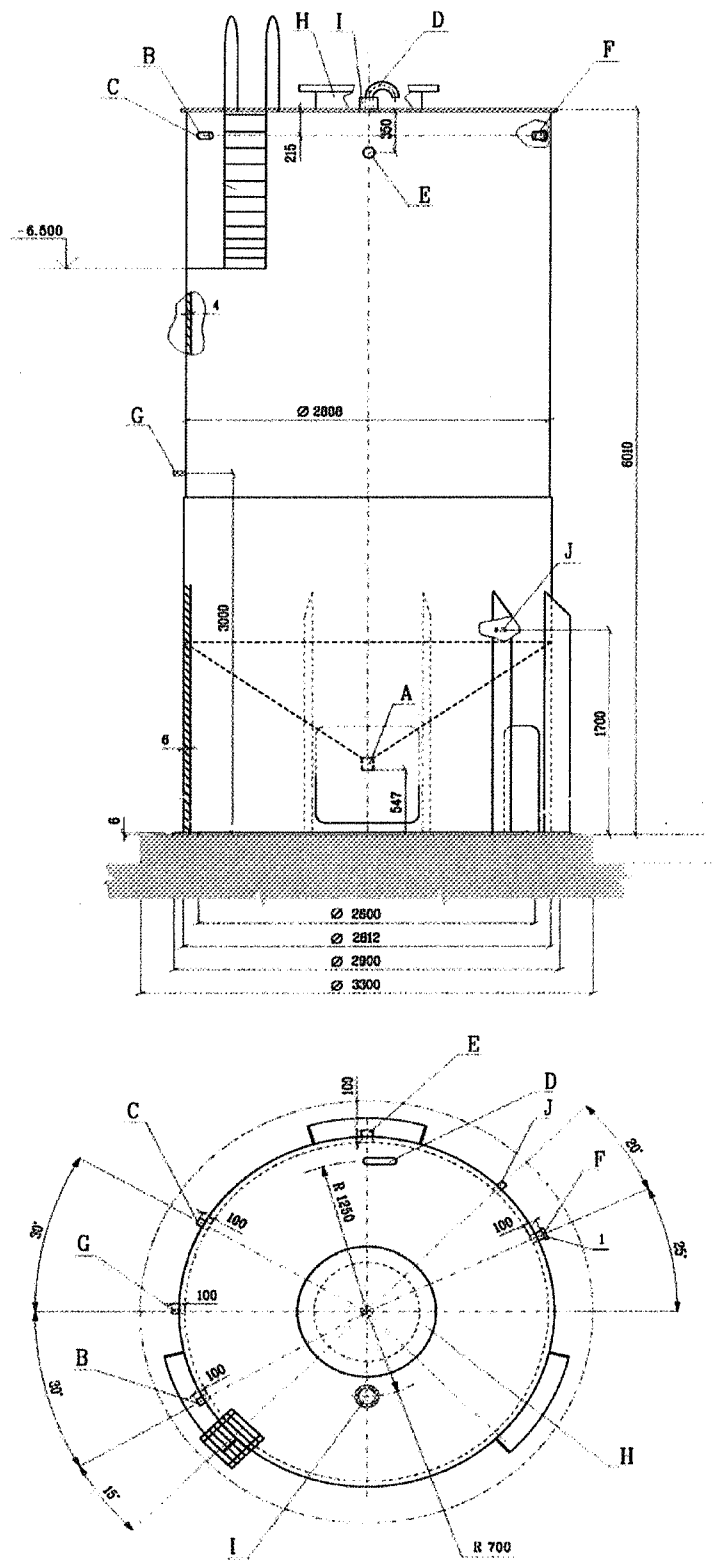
Габаритный чертеж контрольного бака KPF60BV003
